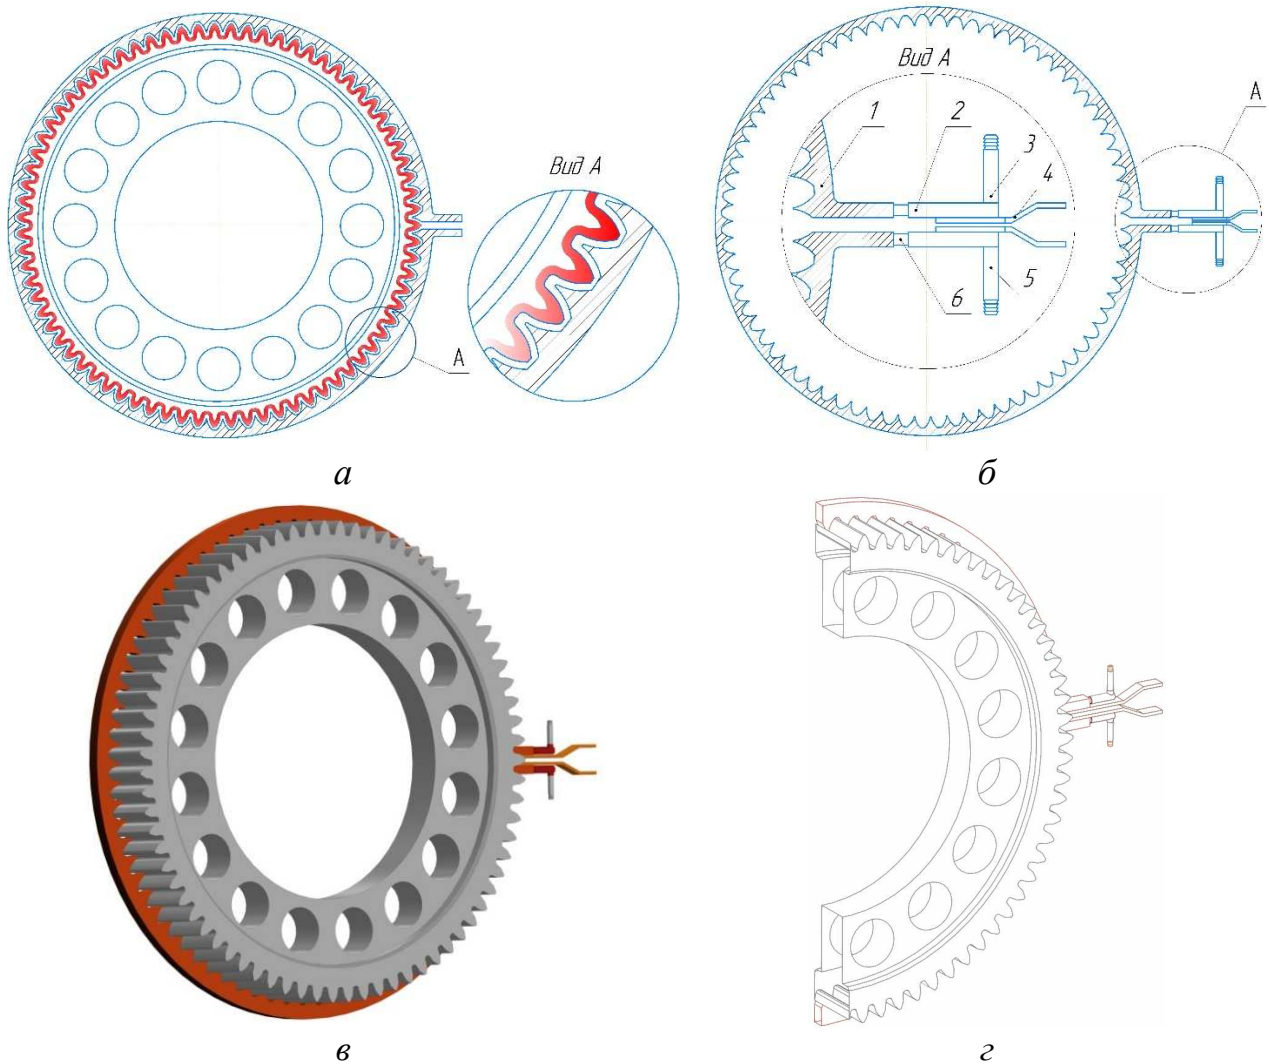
Профильный индуктор для нагрева зубьев венца: а – зона термического влияния; б – конструкция индуктора; в – трехмерная модель индуктора; г – поперечное сечение индуктора; 1 – насадка индуктора; 2 – медная токоведущая трубка; 3 – впускной штуцер; 4 – клемма; 5 – выпускной штуцер; 6 – токопровод
